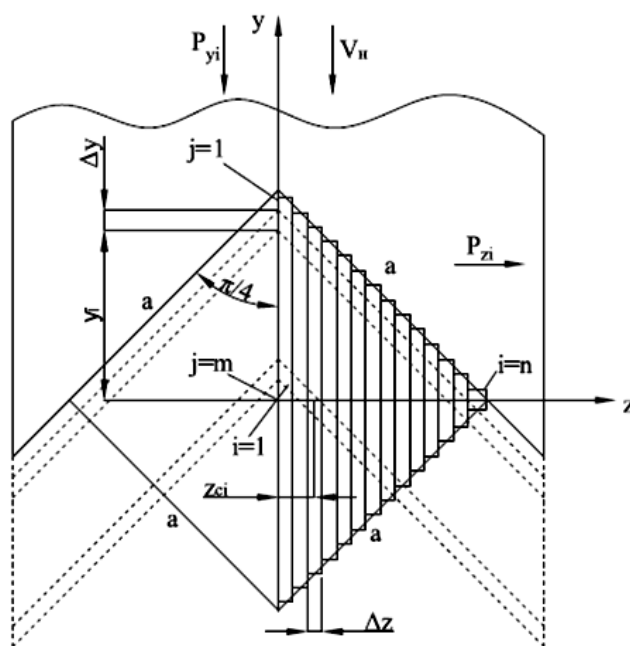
Схема процесса резки на мерные длины непрерывнолитых заготовок
